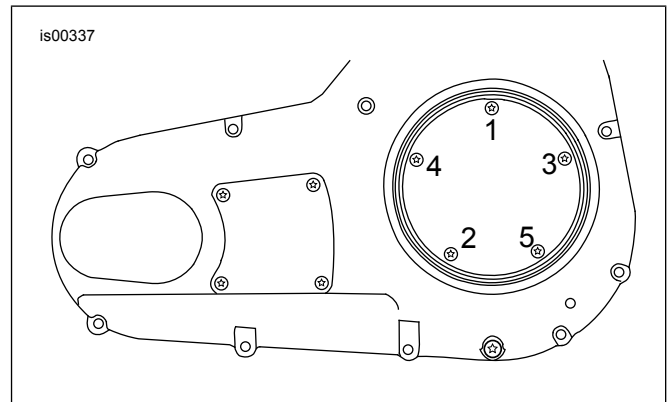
Séquence de serrage, couvercle d'inspection d'embrayage
